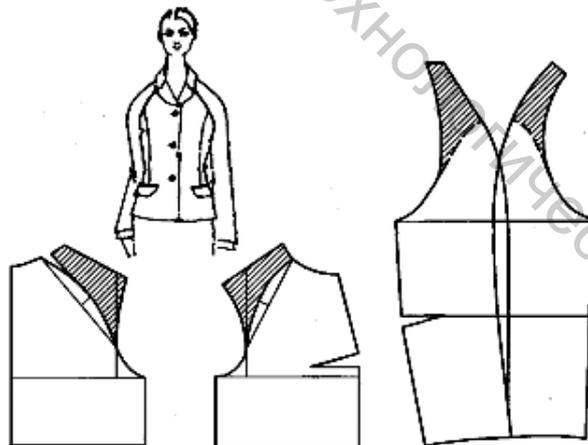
Схема конструкции изделия с рукавам покроя реглан
